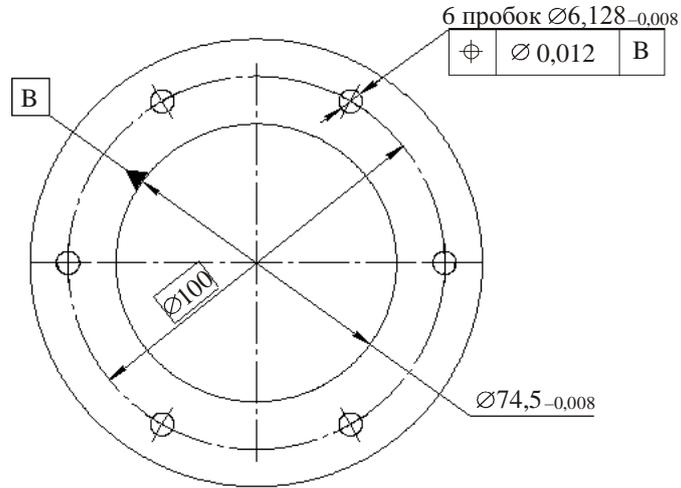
Схема калибра расположения для детали фланца. Размеры изношенных калибров:
